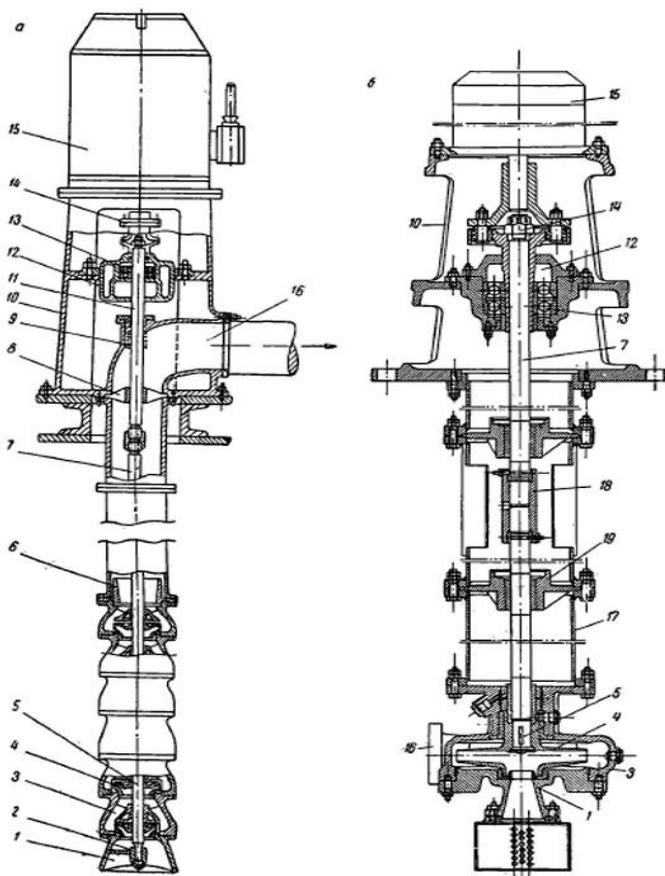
Погружные центробежные насосы для откачки нефтепродуктов из заглубленных резервуаров: а - из вертикальных; б - из горизонтальных. 1 - всасывающий колокол; 2 - втулка колокола; 3 - корпус секции насоса; 4 - рабочее колесо; 5 - вал насоса; 6 - переходник; 7 - вал промежуточный; 8 - крестовина; 9 - сальниковое устройство; 10 - опорная стойка; 11 - вал опорной стойки; 12 - корпус подшипника; 13 - шариковый подшипник; 14 - соединительная муфта; 15 - вертикальный взрывобезопасный асинхронный электродвигатель; 16 - напорный патрубок; 17 - напорная колонна; 18 - соединительная муфта; 19 - промежуточный подшипник.
